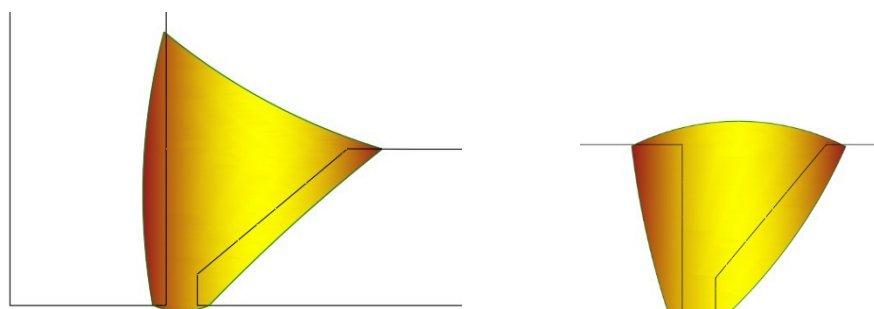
Зварні шви для з'єднання 1.9.1
